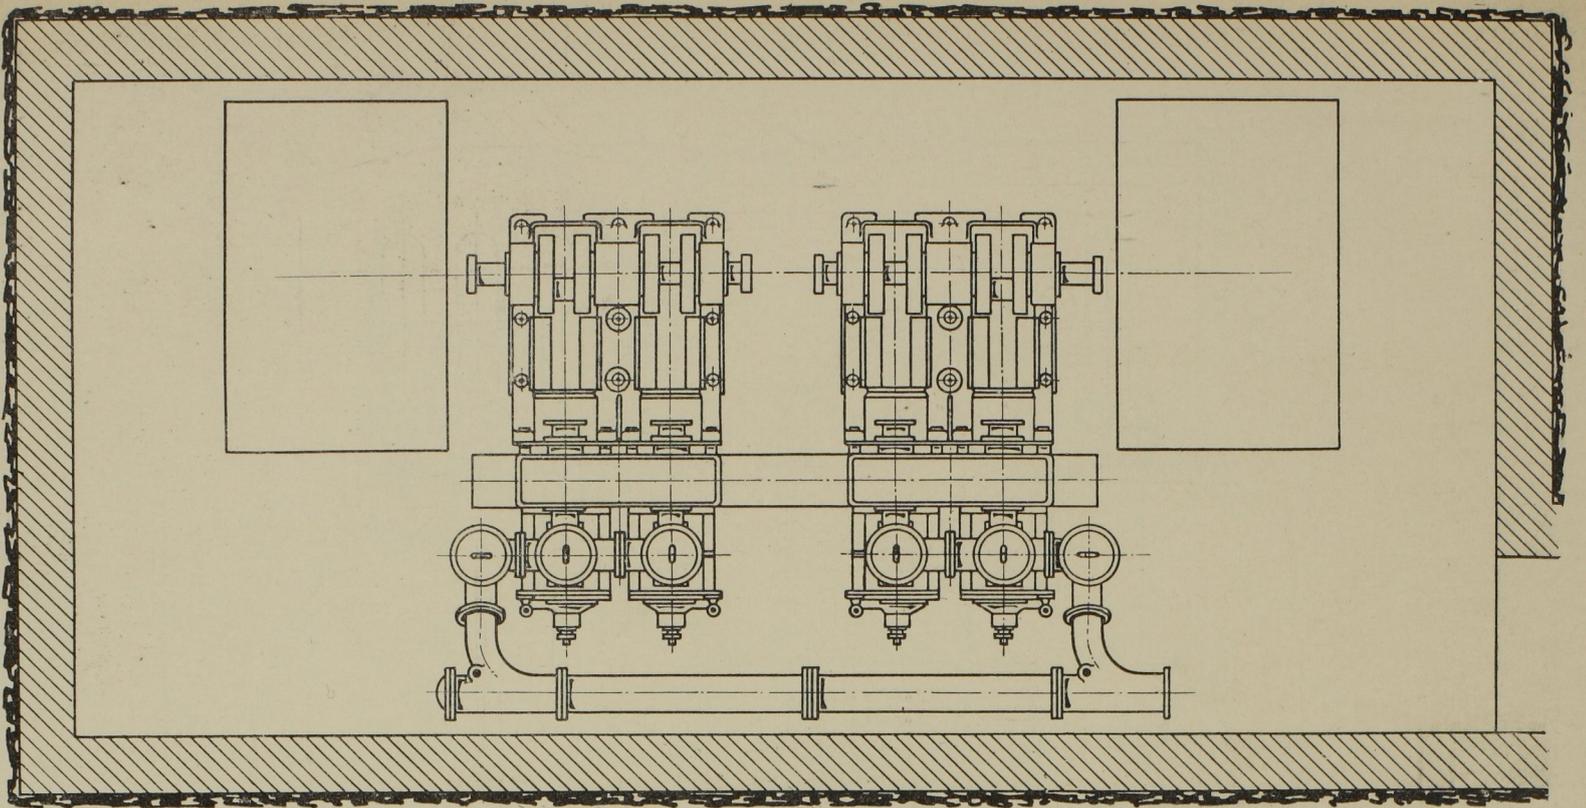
Grundriss der beiden Wasserhaltungsmaschinen. Masst. 1:80.
